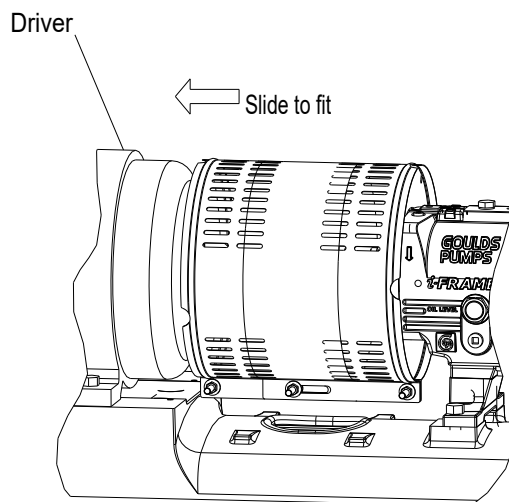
Skjut kopplingskyddets motorhalva mot motorn
